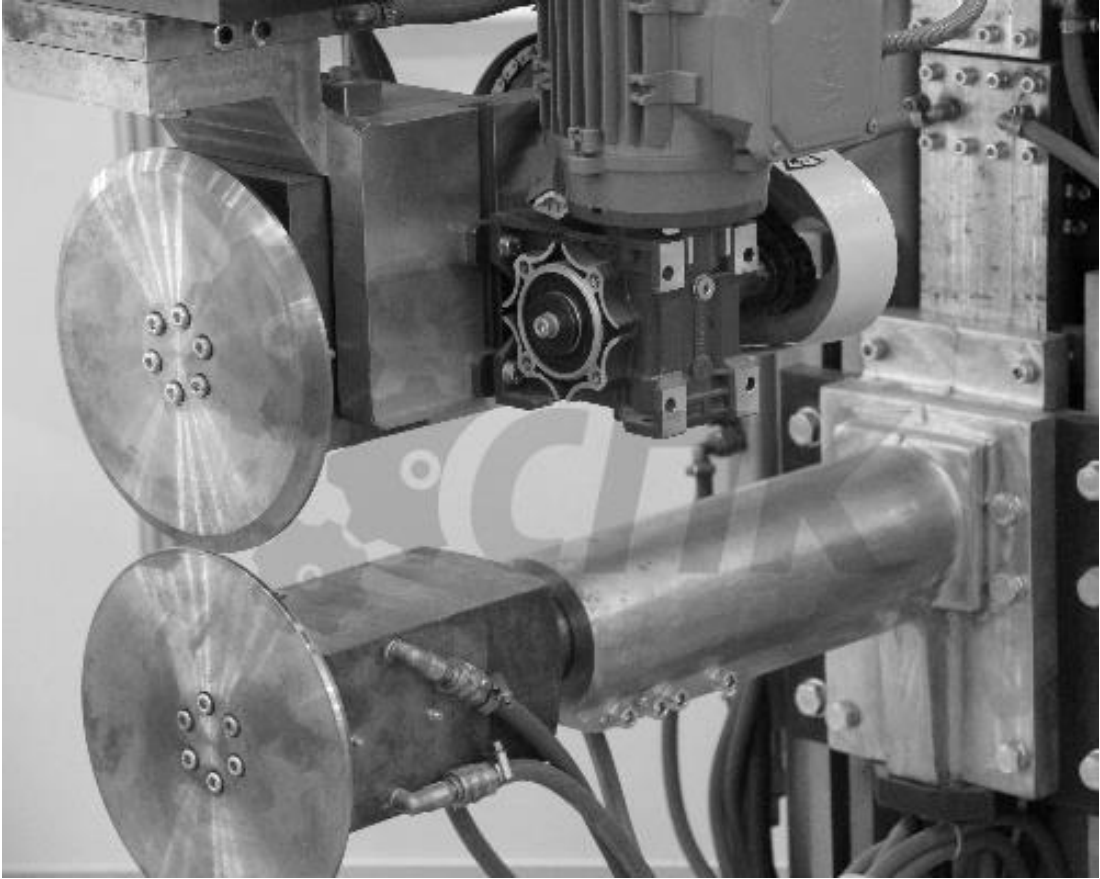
Загальний вигляд роликів шовного контактної зварювання
